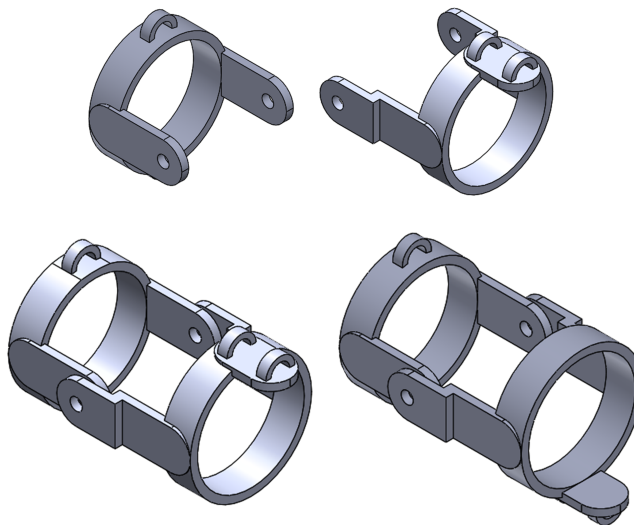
Pièces du pouce séparées et assemblées
